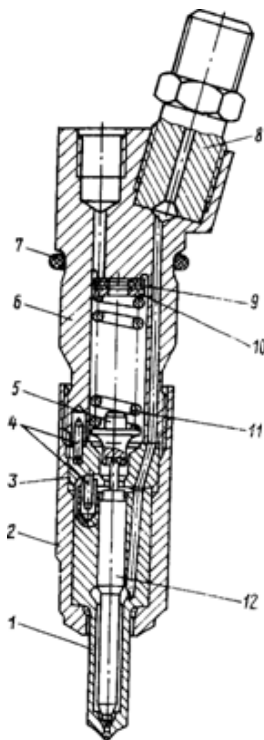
Форсунка: 1 – корпус распылителя; 2 – гайка распылителя; 3 – проставка распылителя; 4 – штифты установочные; 5 – штанга форсунки; 6 – корпус форсунки; 7 – кольцо уплотни- тельное; 8 – штуцер; 9, 10 – шайбы регулировочные; 11 – пружина форсунки; 12 – игла распылителя
